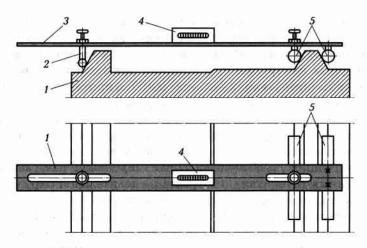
Универсальный контрольный мостик для проверки параллельности направляющих токарного станка:
